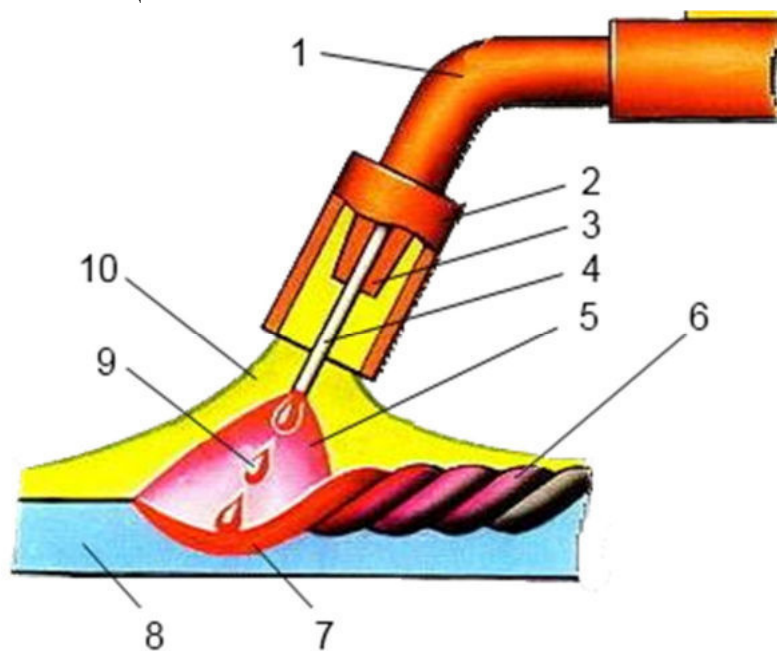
Схема полуавтоматической сварки (MIG/MAG).
